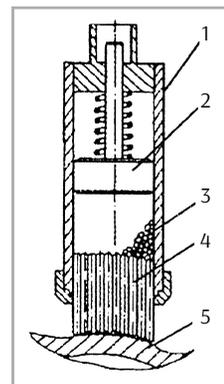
Схема шарикостержневого упрочнителя: 1 – корпус; 2 – боек; 3 – стальные шарики; 4 – стержни; 5 – обрабатываемая поверхность
